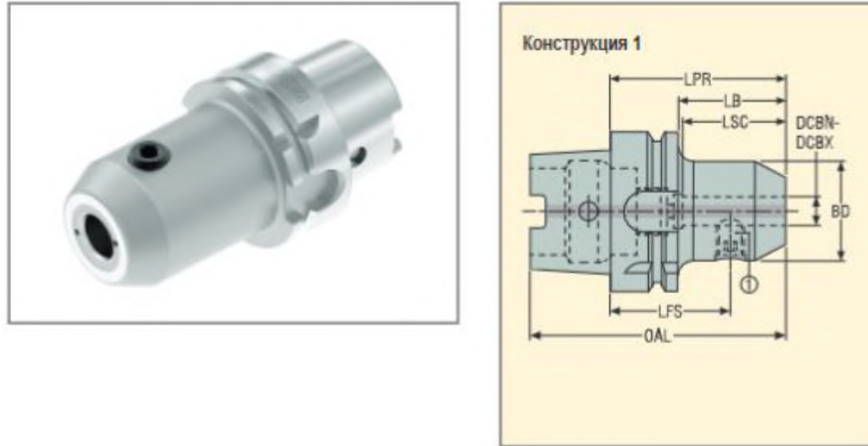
Weldon DIN 1835 (HKA63-EM10-065-L1) з конусом шпинделя HSK-A63 [6 с.78]
